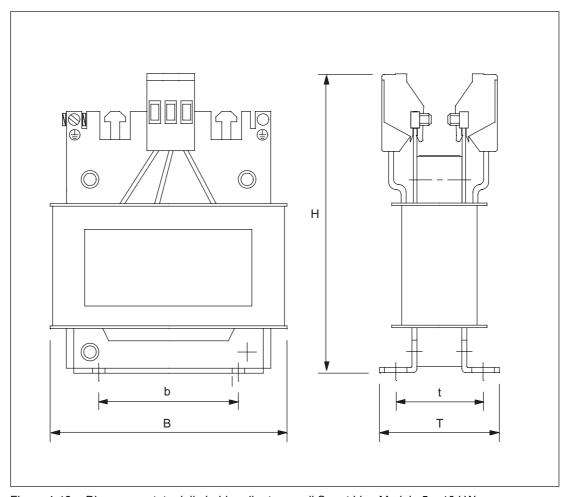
Disegno quotato della bobina di rete per gli Smart Line Module 5 e 10 kW
